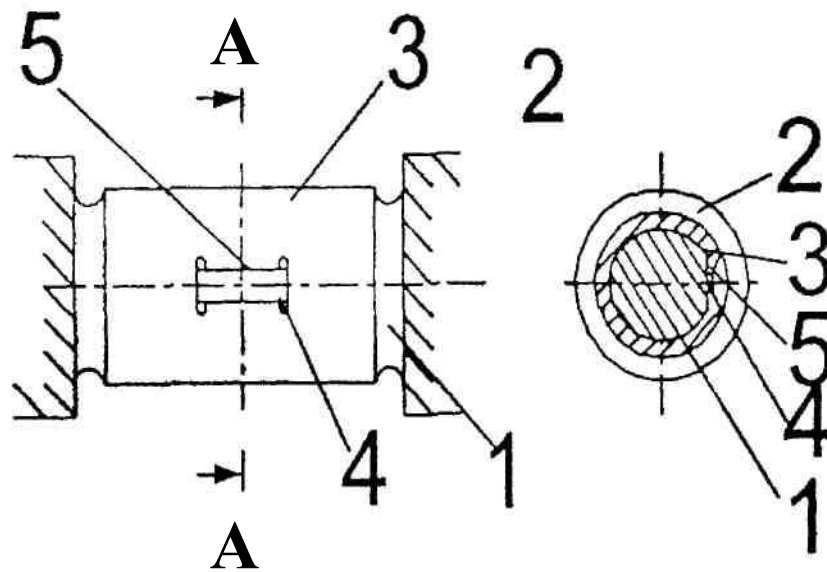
Схема відновленої шийки в зборі: 1-шийка, 2-колінчатий вал, 3-оболонка, 4-перемичка, 5-виступи.
